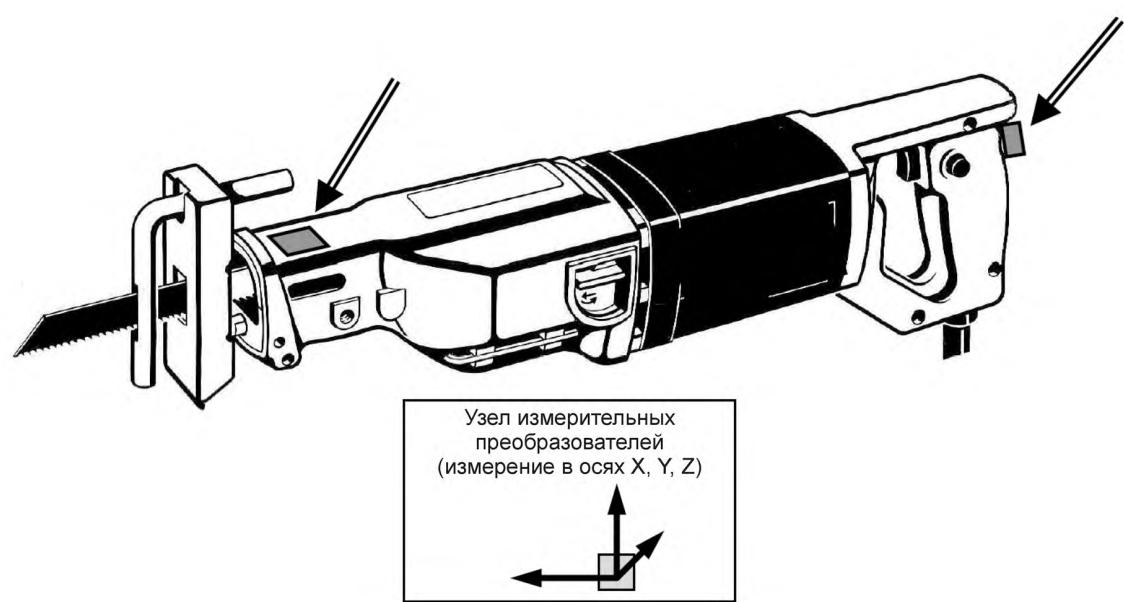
Расположение измерительных преобразователей для ножовочных пил
